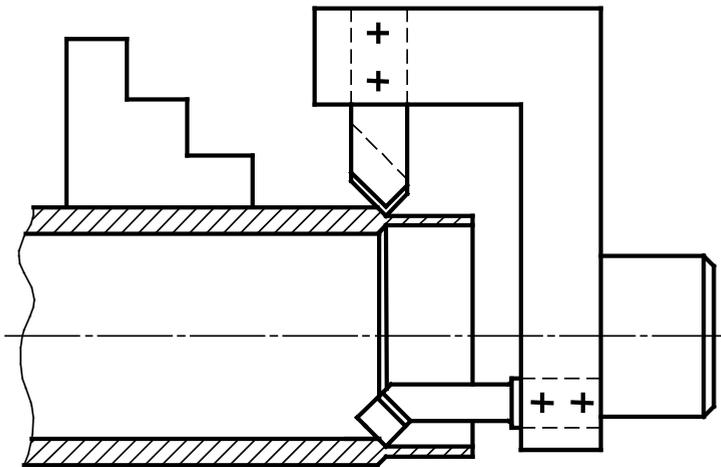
Схема обработки втулки на токарно-револьверном станке при совмещении настроечной и измерительной баз
